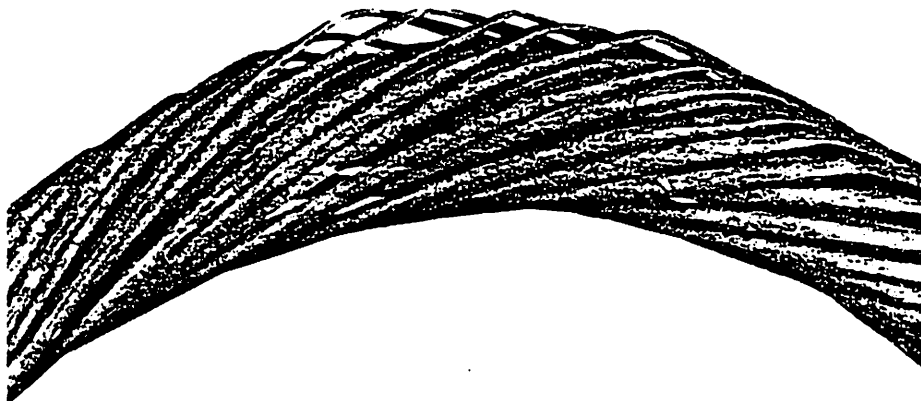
Drahtseil mit durch Korrosion und Abrieb gelockerten Drähten
